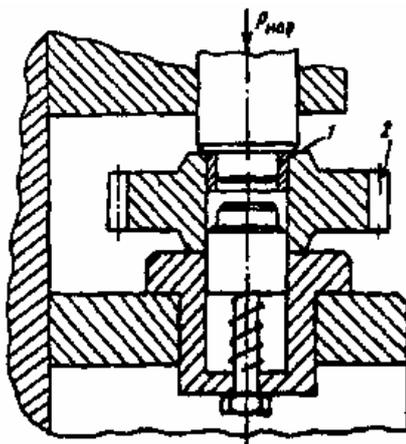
Схема приспособления для ориентации и запрессовки втулки 1 в шестерню 2
